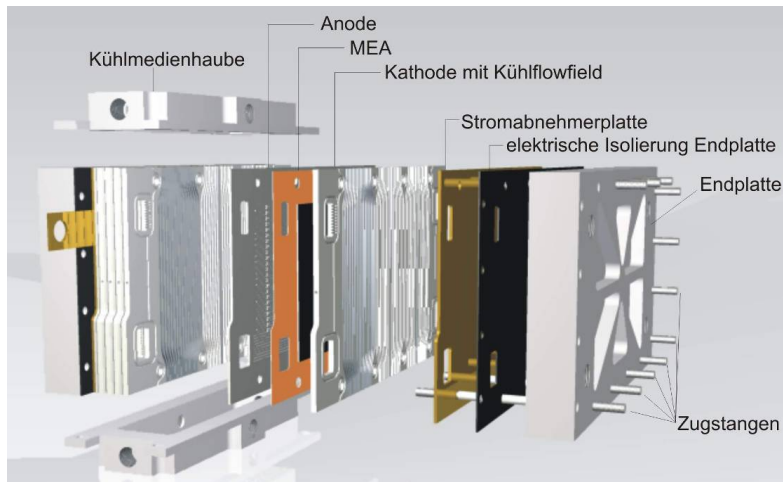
Explosionszeichnung eines HT-PEFC-Stacks vom IEF-3 [195]
